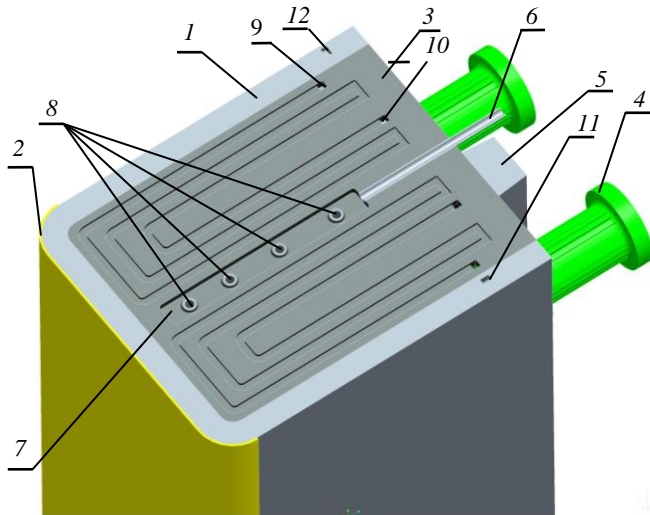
Поперечный разрез КЛС ИМБ по каналам охлаждения верхней крышки: 1 — скоба ПС; 2 — защитное бериллиевое покрытие; 3 — верхняя крышка корпуса ИМБ; 4 — гибкая механическая опора; 5 — верхний противомоментный ключ; 6 — входной патрубок газа-носителя; 7 — входной коллектор газа-носителя; 8 — входные трубки газа-носителя в ЗВТ; 9 — вход теплоносителя в канал охлаждения крышки; 10 — выход теплоносителя из канала охлаждения крышки; 11 — вход теплоносителя в канал охлаждения фланца скобы ПС; 12 — выход теплоносителя из канала охлаждения фланца скобы ПС
